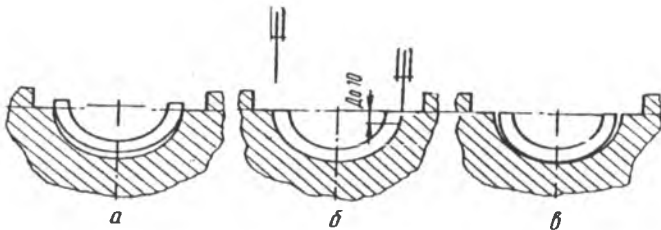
Пригонка вкладышей коренных подшипников по по-
